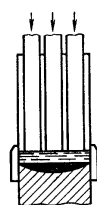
Схема сварки электродами большого сечения с применением в качестве электрода трех пластин сплошного сечения
